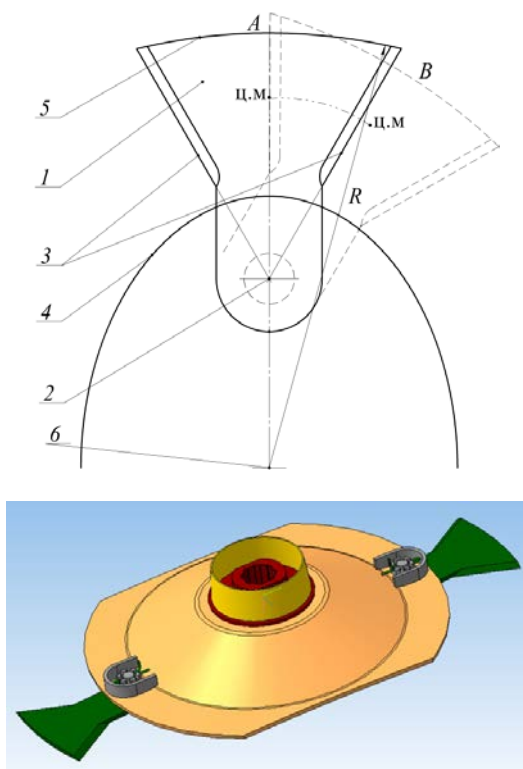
Конструкция трапециевидного ножа роторной косилки:
